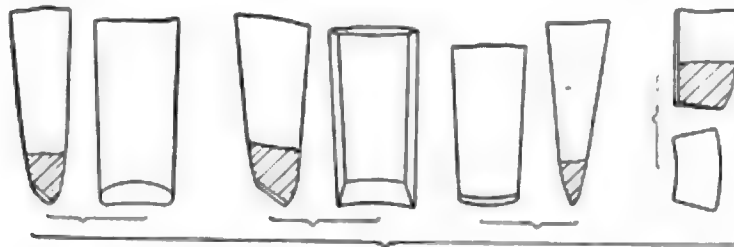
Werkzeuge zum Verstemmen der Nietköpfe.
